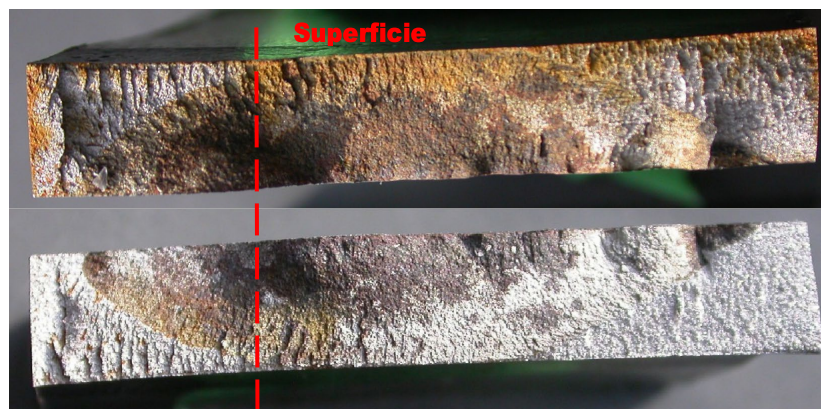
Caño 48330. Defecto 1_1, pasante. Superficie de fractura. Se observan marcas de playa. Línea punteada indica zona de corte para probeta metalográfica.
